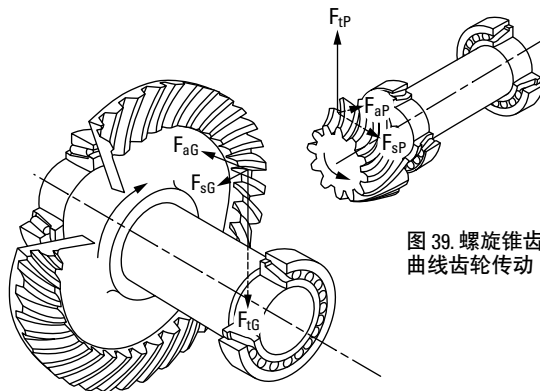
螺旋锥齿轮和准双曲面曲线齿轮传动
